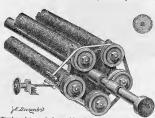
Tambour laineur de la machine Grosselin; extrémité portant la courrcie ; de commande. Coupe d'un travailleur.
